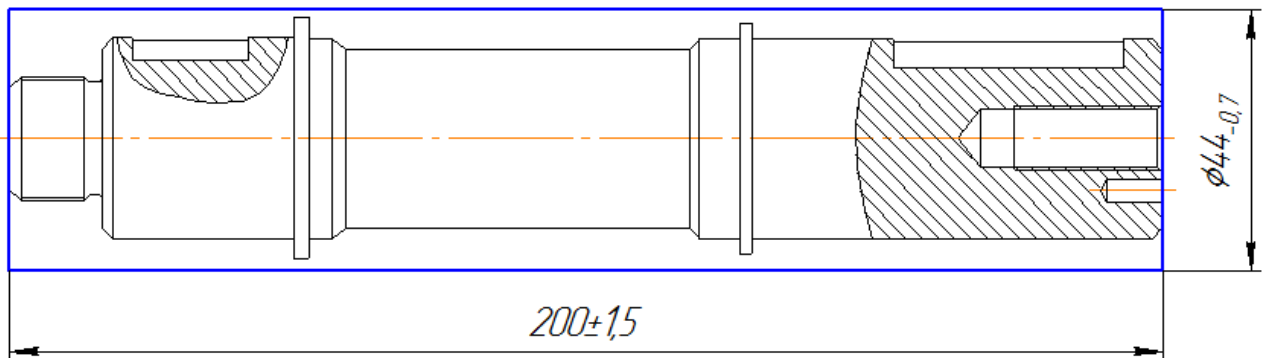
Ескіз заготовки отриманої прокату розрізаного пилою
